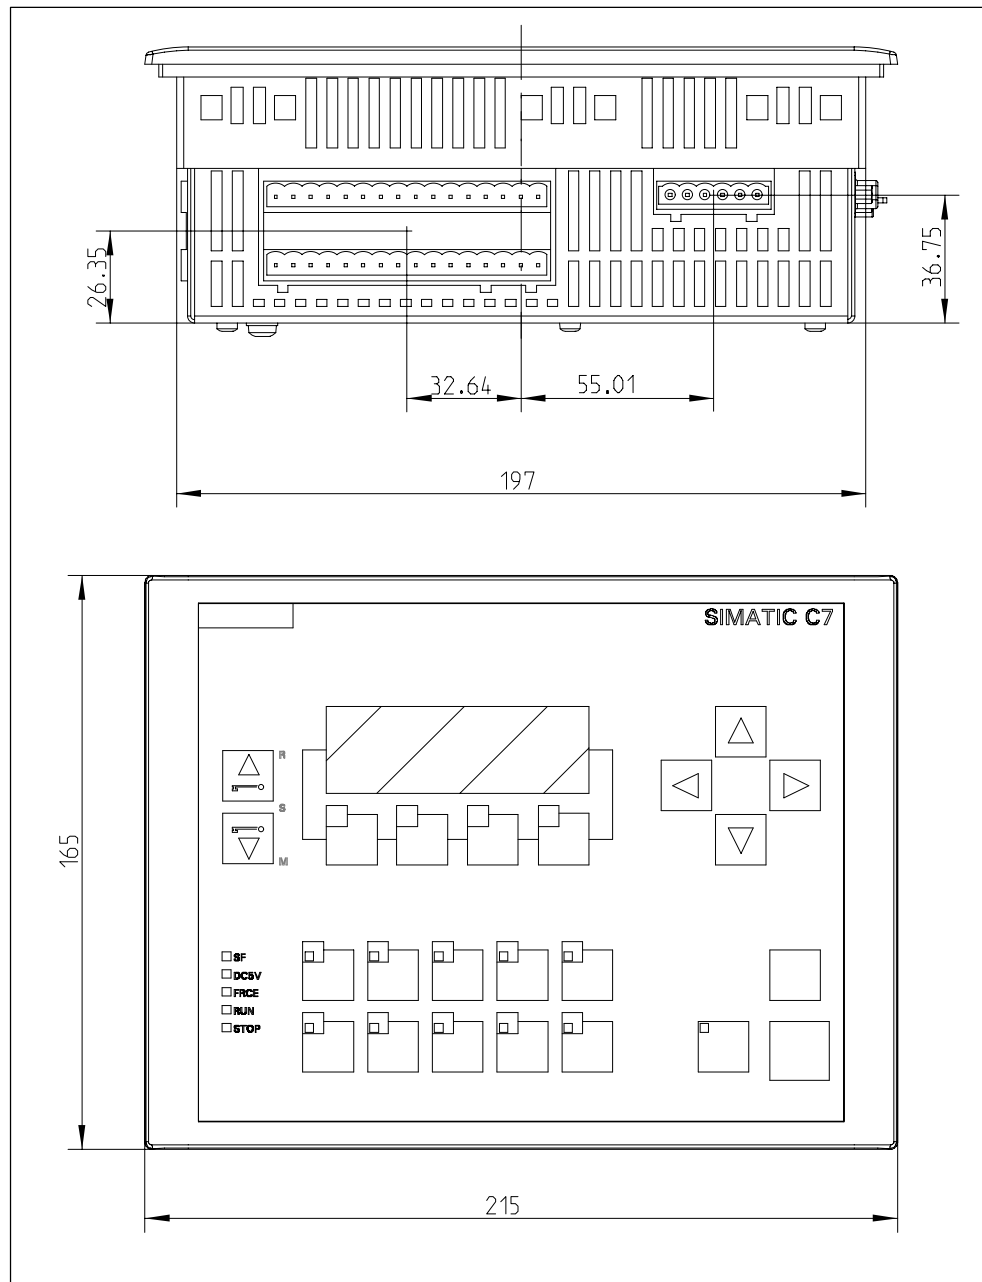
Maßbilder für das C7-613 (Maße in Millimeter)
